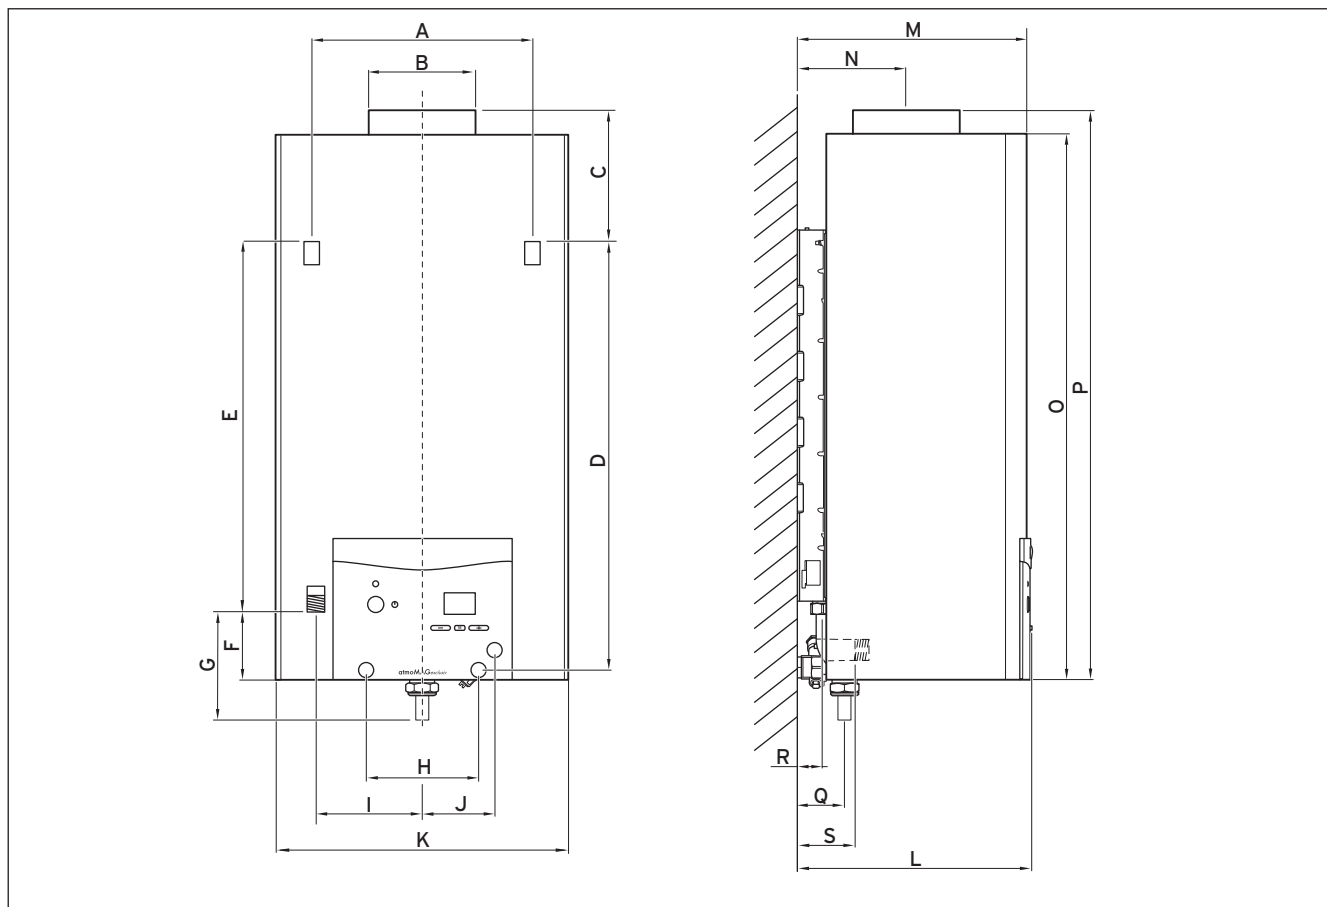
Desenho das dimensões do atmoMAG exclusiv
